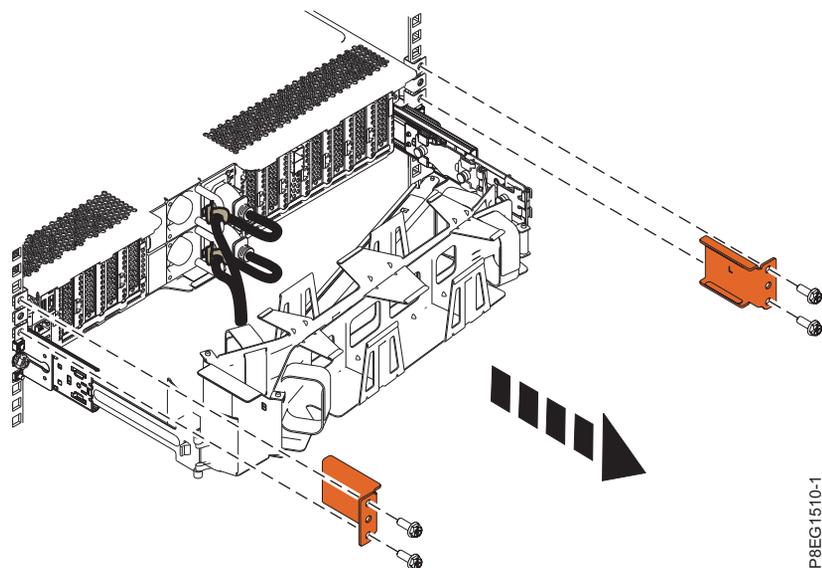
Removendo os suportes de remessa da parte traseira do chassi
